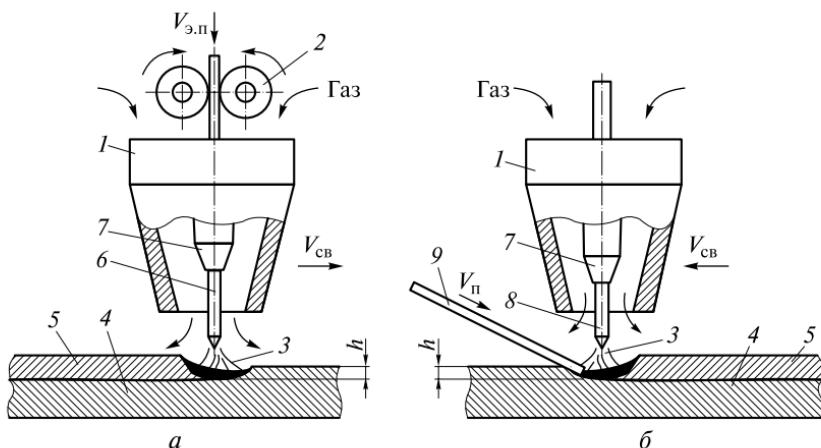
Схема сварки в защитном газе плавящимся (а) и неплавящимся (б) электродами:
